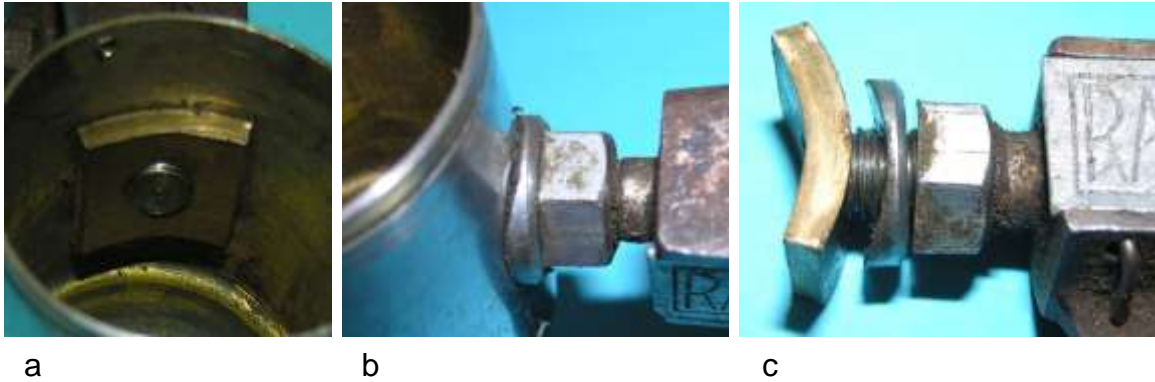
Befestigung des Drehbolzens am Gehäusemantel: a) Spannmutter innerhalb des Gehäuses, b) Gekrümmte Scheibe und Kontermutter, c) Drehbolzen mit Spannmutter, gekrümmter Scheibe und Kontermutter
